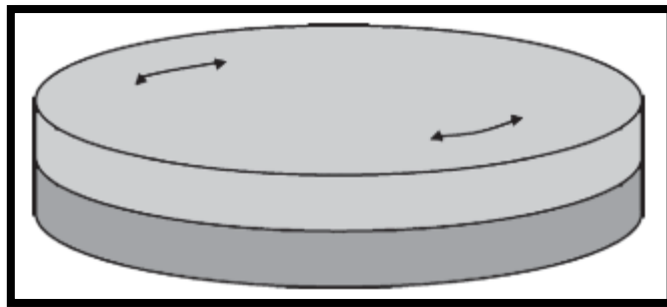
Descripción de una máquina de soldadura por fricción orbital
